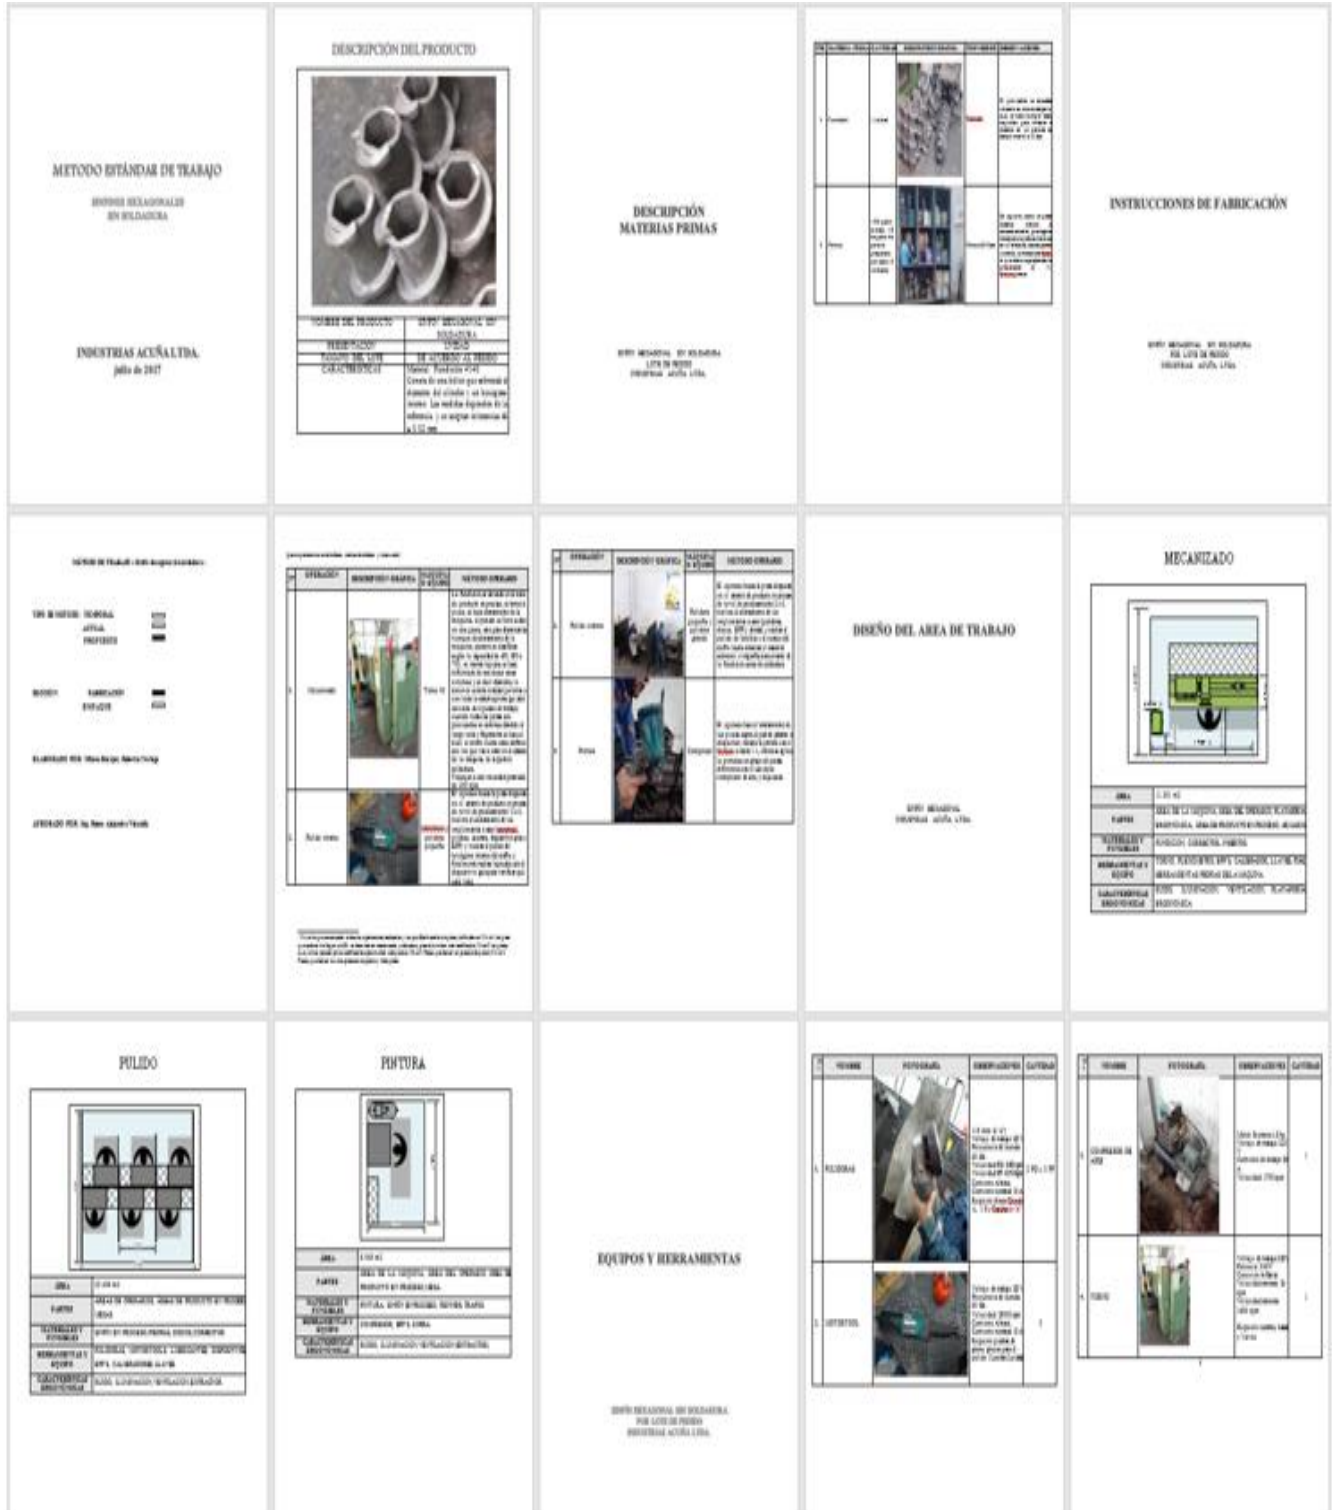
Método estándar de fabricación-Sinfines sin soldadura.
